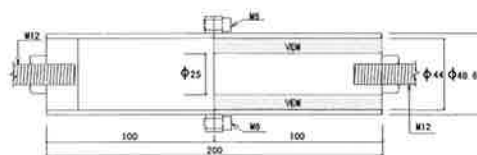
筒型ダンパー小型試験体断面図 [単位:mm]
